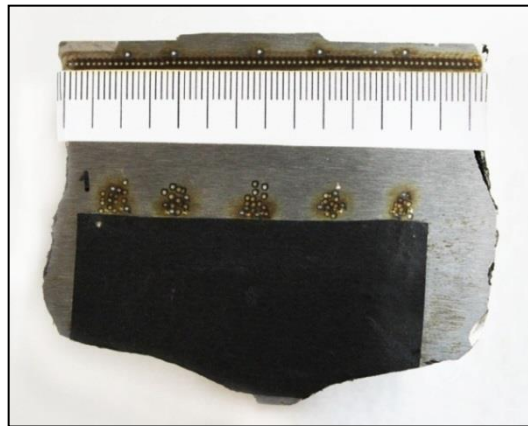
Фото продольного сечения сварного шва двух рельс (слева направо: рельс 1, область сварки, рельс 2). Шаг шкалы – 1 мм, диаметр пятна лазера ~0.4 мм.
